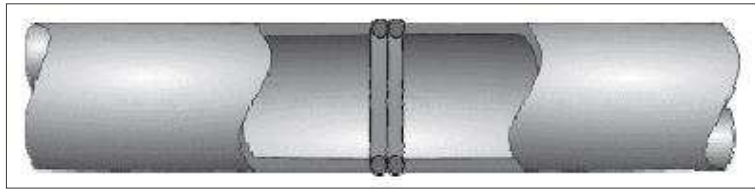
Illustration d'une soudure par soudage bout à bout standard. (Source : Handbook of polyethylene pipe – second edition)
